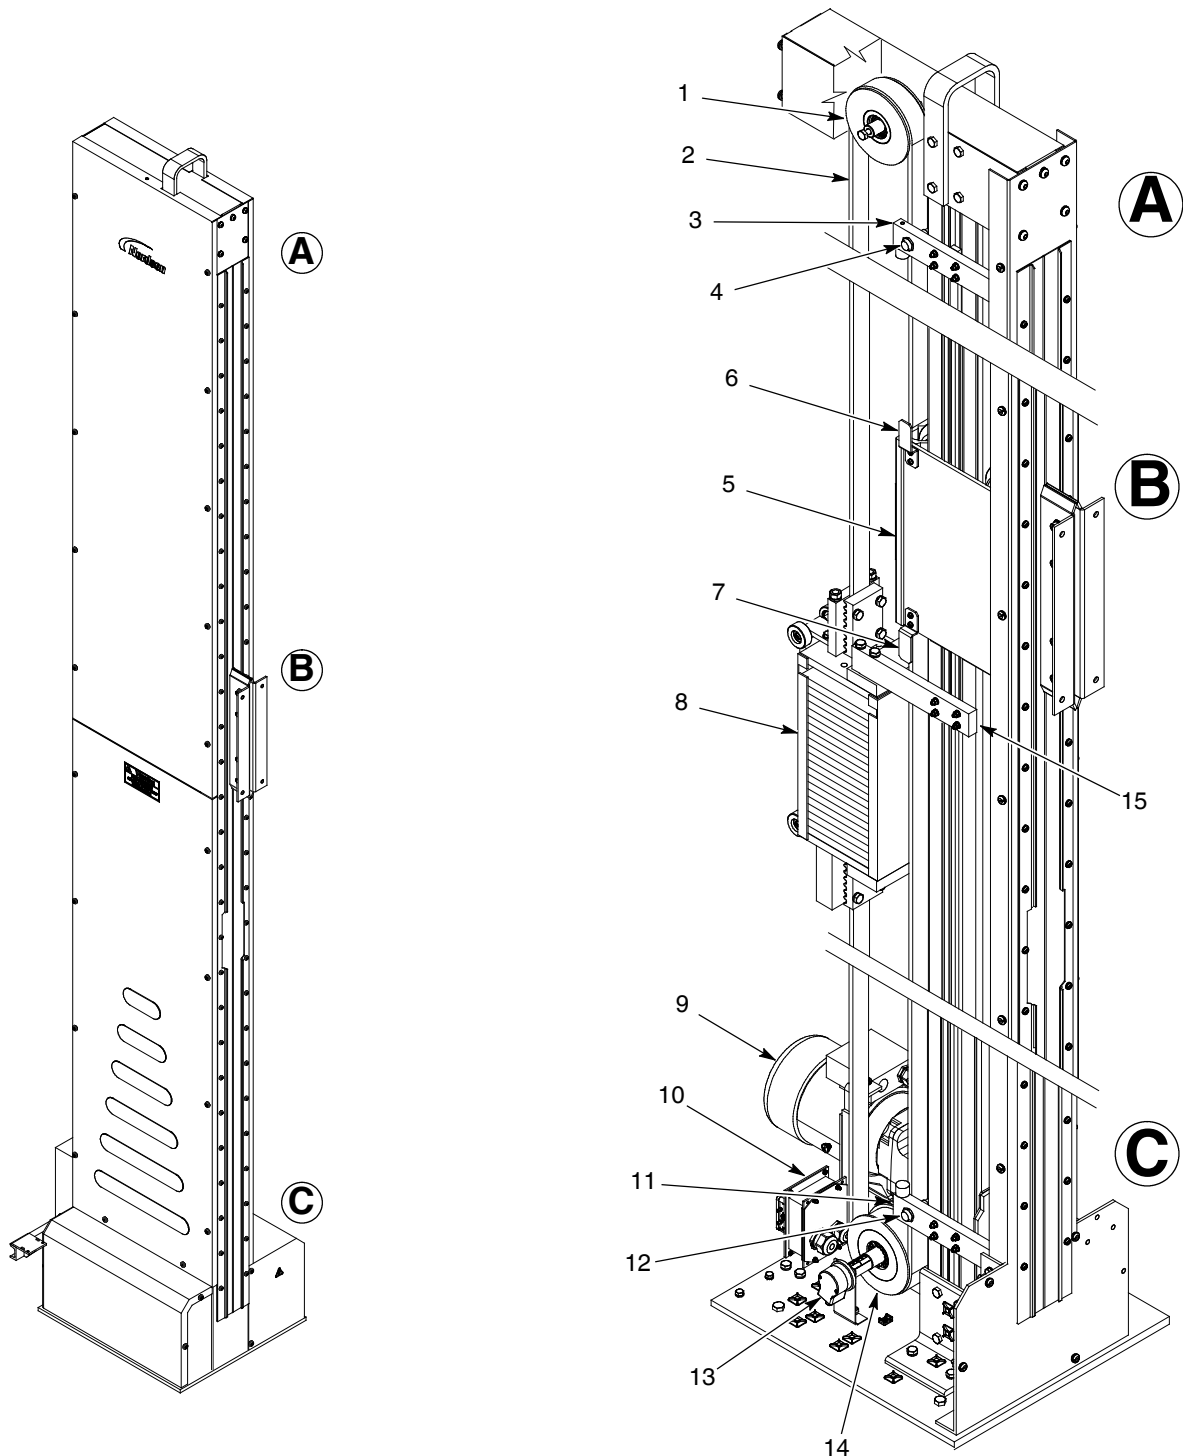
Типовой вертикальный возвратно-поступательный манипулятор NVR
